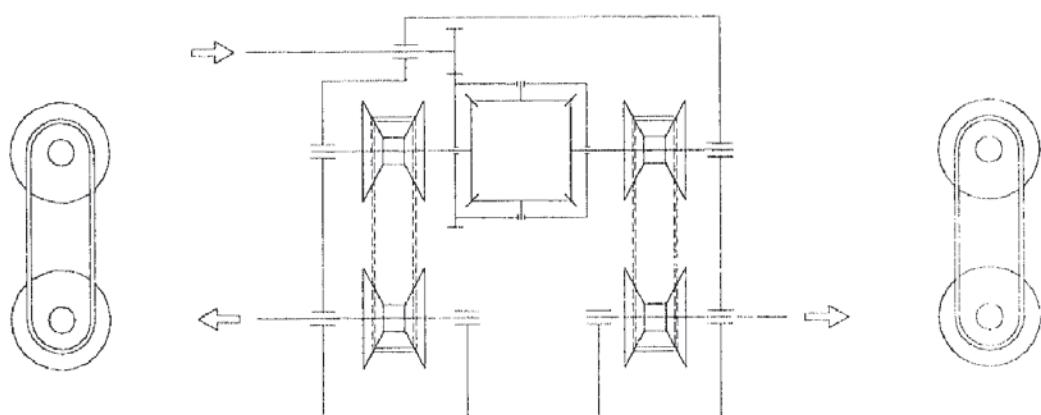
Схема раздаточной коробки с двумя вариаторами
